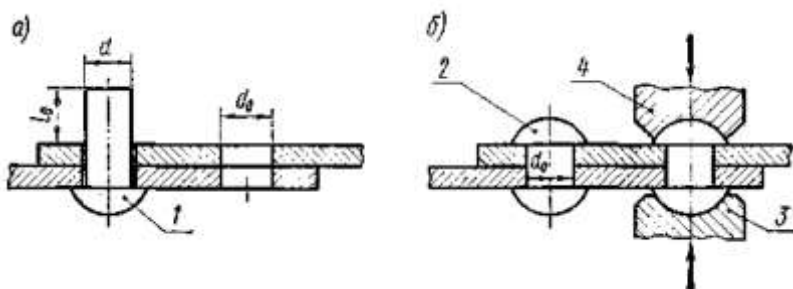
Образование заклепочного шва: а – закладка заклепки; б – клепка
